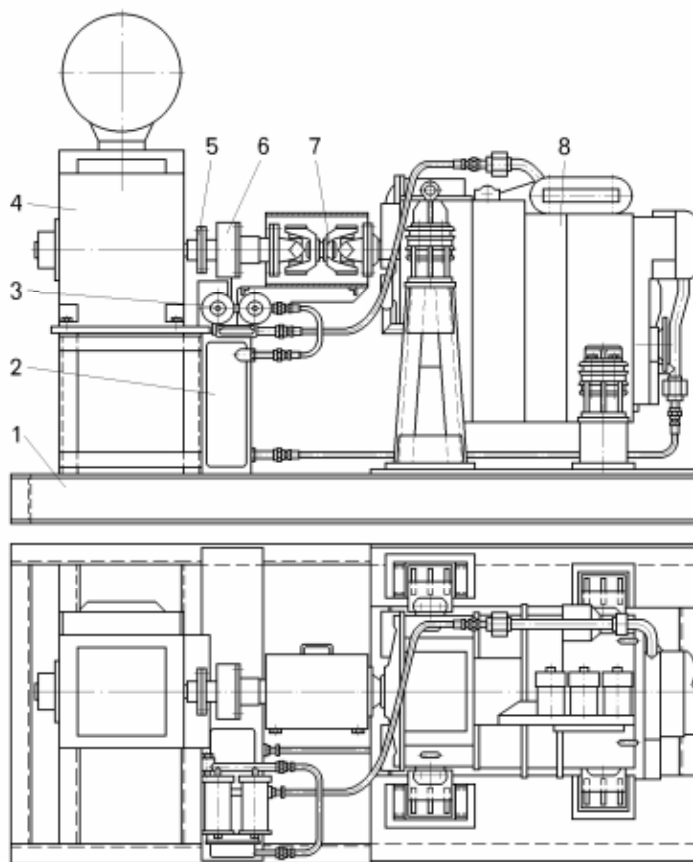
Стенд для обкатки и испытания гидромеханической передачи (без нагрузки):
